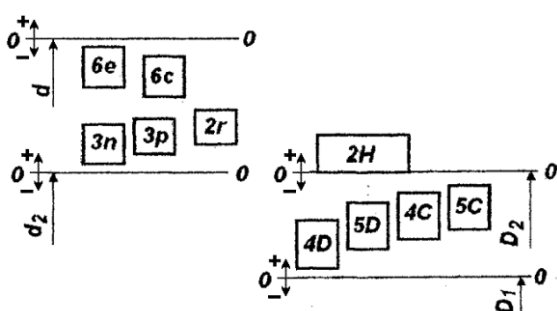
Розташування полів допусків різьби з натягом.
